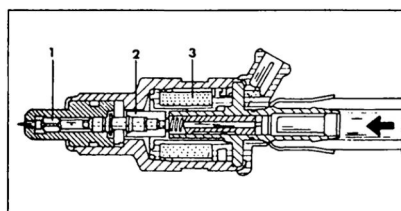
Форсунка. 1 - игла распылителя, 2 - магнитный якорь, 3 - обмотка магнита.
